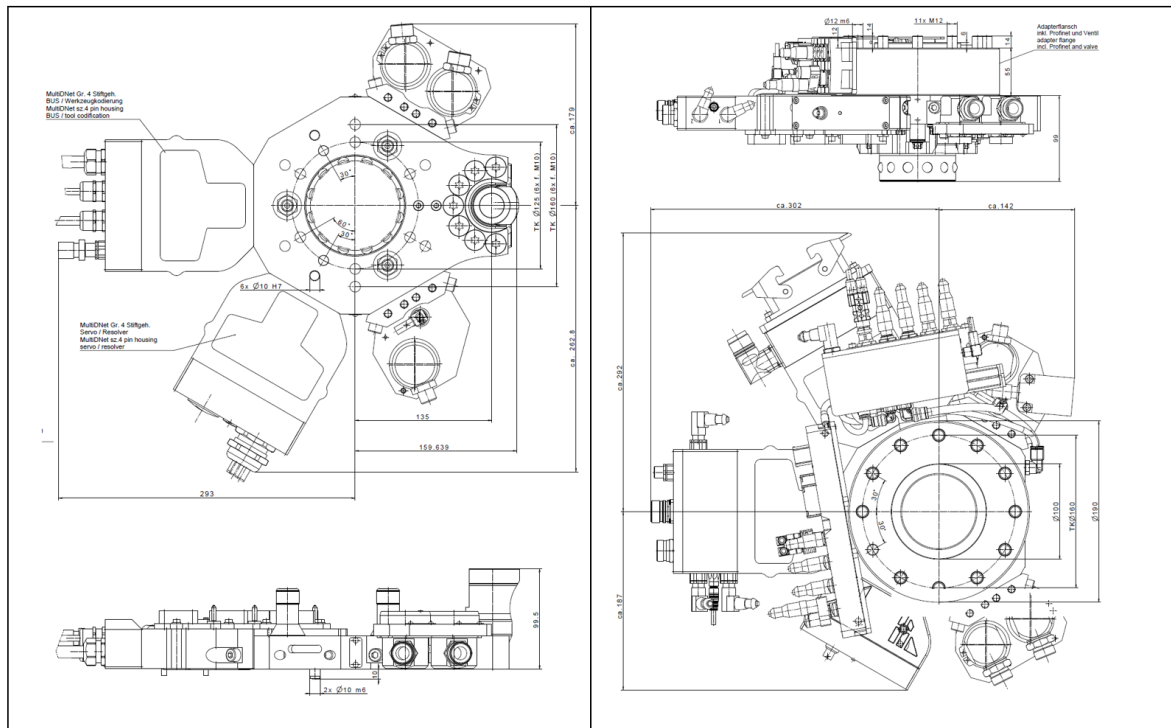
Zeichnung des Werkzeugwechslers: Werkzeugseite (li.) und Roboterseite (re.).
